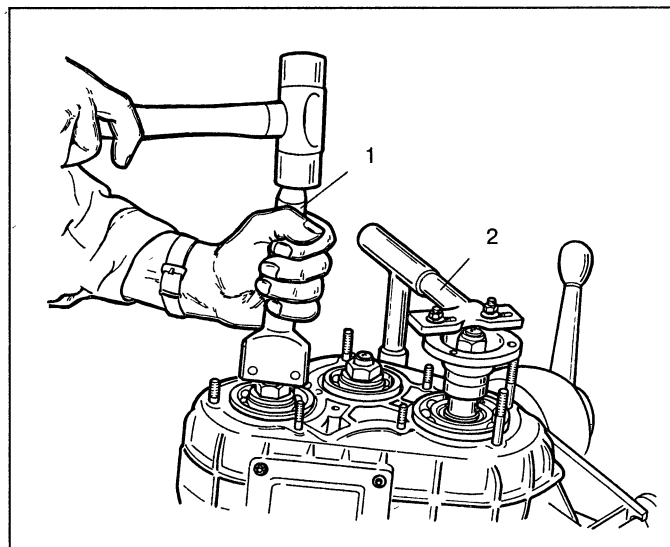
Обжатие гайки крепления фланца вала привода заднего моста: 1 – оправка 67.7820.9520; 2 – фиксатор фланца
